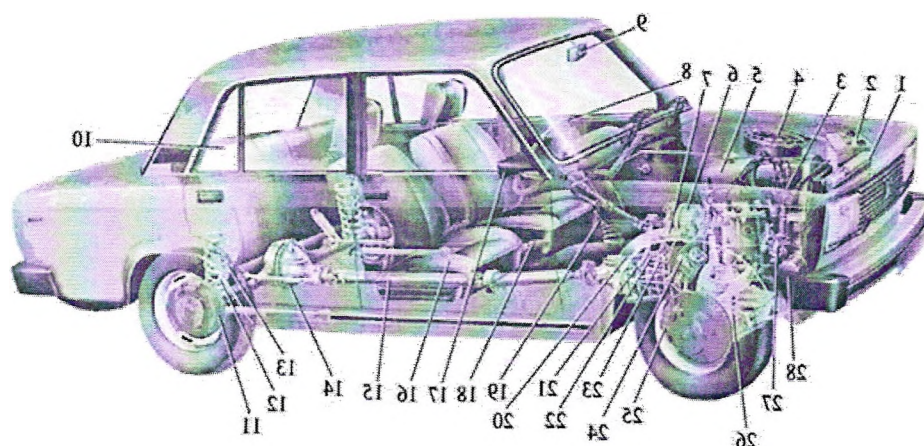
Общий вид легкового автомобиля: 1 — радиатор системы охлаждения; 2 — аккумуляторная батарея; 3 — распределитель зажигания; 4 — воздушный фильтр; 5 — двигатель; 6 — вакуумный усилитель с главным цилиндром гидропривода тормозов; 7 — главный цилиндр гидропривода сцепления; 8 — рулевое колесо; 9 — внутреннее зеркало заднего вида; 10 — заднее сиденье; 11 — задний тормоз; 12 — пружина задней подвески; 13 — амортизатор задней подвески; 14 — задний мост; 15 — карданная передача; 16 — переднее сиденье; 17 — наружное зеркало заднего вида; 18 — рычаг стояночного тормоза; 19 — рычаг переключения передач; 20 — коробка передач; 21 — педаль сцепления; 22 — педаль тормоза; 23 — педаль акселератора («газа»); 24 — картер рулевого механизма; 25 — передний тормоз; 26 — пружина передней подвески с амортизатором; 27 — топливный насос; 28 — масляный фильтр
